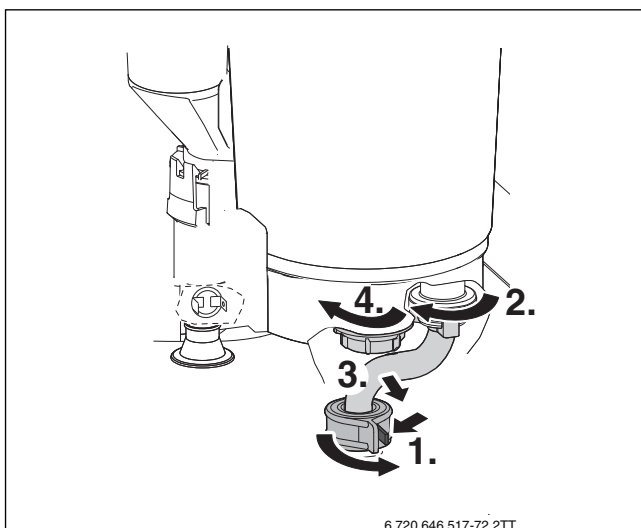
Mutter entfernen und Rücklaufrohr lösen
